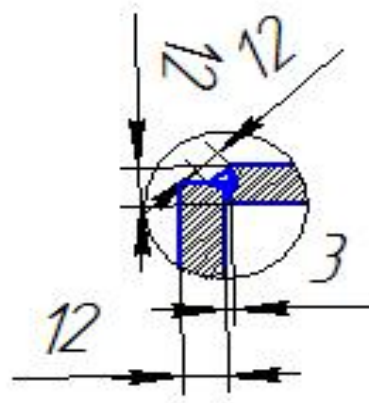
Параметры сварного шва соединения Н1
